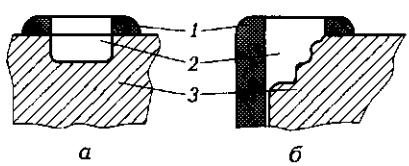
Формы, применяемые при дуговой сварке деталей из чугуна:
